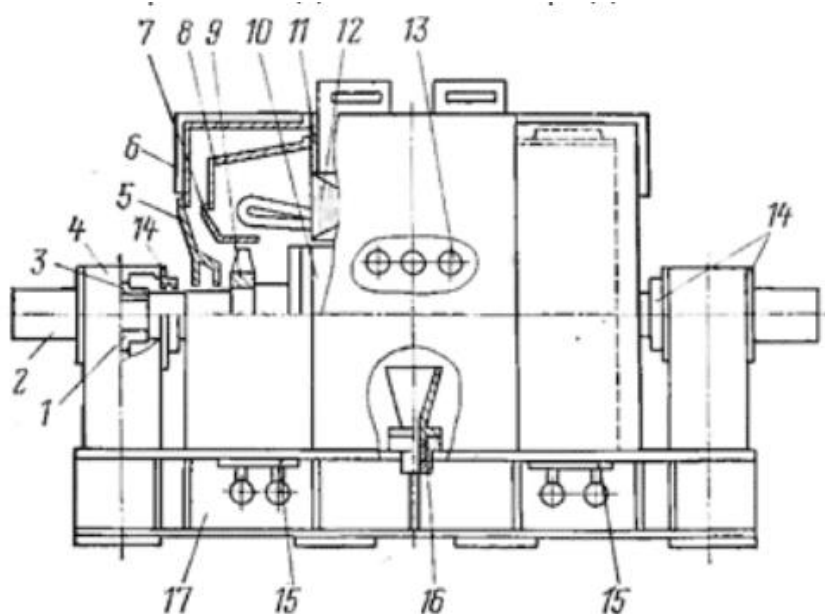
Двигун 2АЗМ 5000/6000: 1 - нижній вкладиш підшипника, 2 - вал, 3 - верхній вкладиш підшипника, 4 - кришка підшипника; 5 - повітрянаправляючий зовнішній щит, 6 – кожух, 7 – дифузор, 8 - повітрянаправляючий внутрішній щит, 9 – вентилятор, 10 - сердечник ротора, 11 - корпус статора, 12 сердечник статора, 13 - ізолятори ввідного пристрою, 14 - лабіринтові ущільнення, 15 – повітроохолоджувач, 16 - ввідний пристрій, 17 - монтажна плита.
